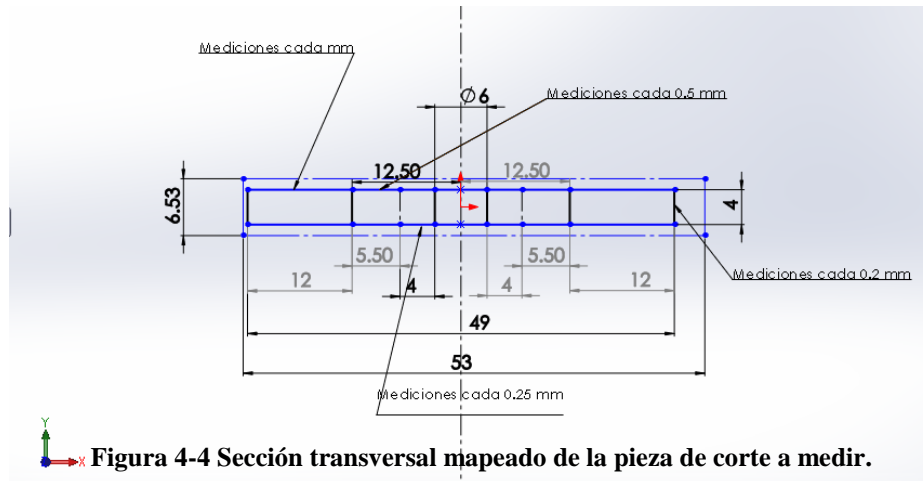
Sección transversal mapeado de la pieza de corte a medir.
